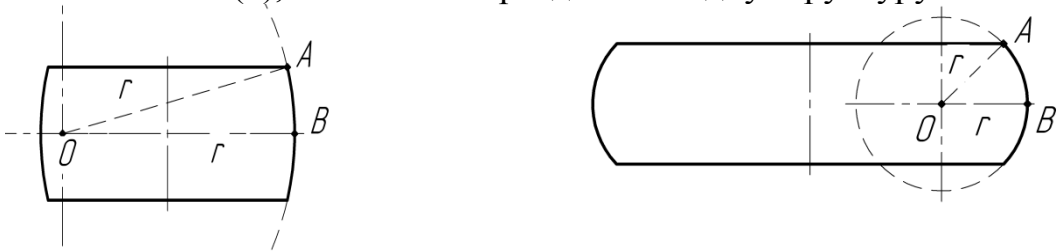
Побудова форми бічної поверхні циліндричної заготовки при осадженні у вигляді частини кола
